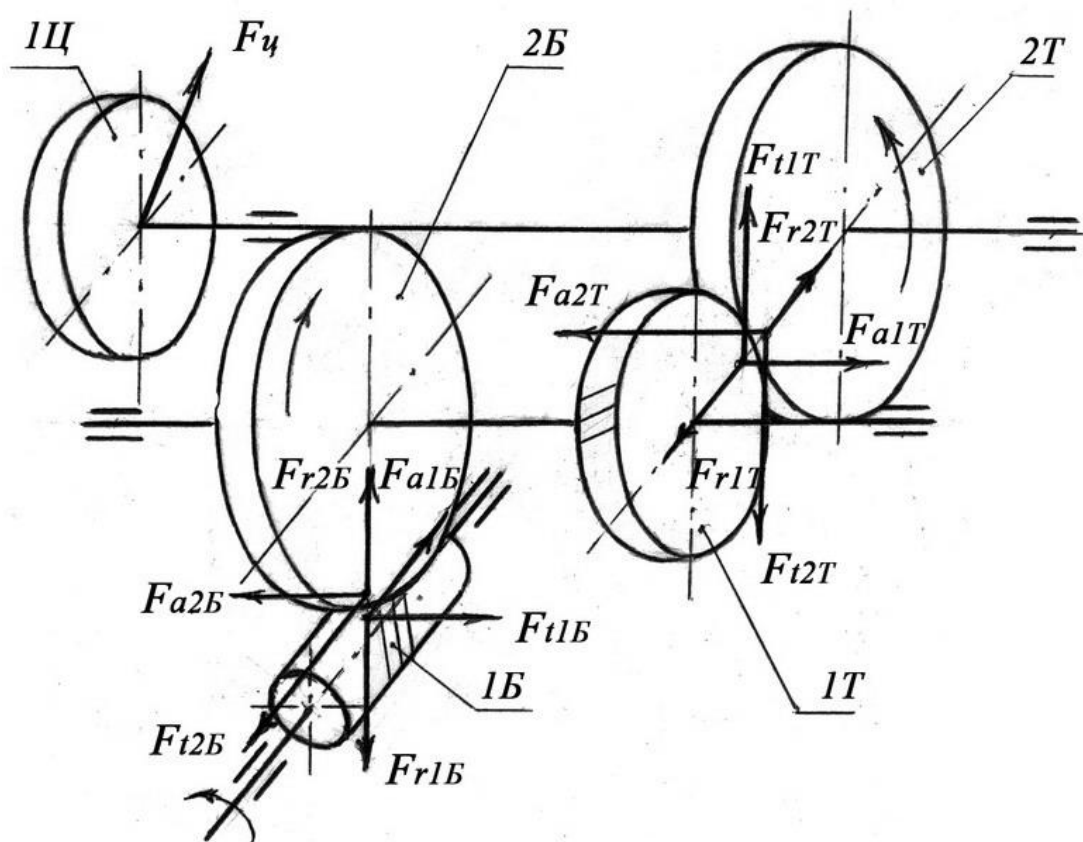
Кинематическая схема червячно-цилиндрического редуктора с силами в зацеплениях быстроходной (Б) и тихоходной (Т) передач на ведущих (1) и ведомых (2) звеньях, а также на ведущей звездочке (1Ц) от действия цепной передачи
